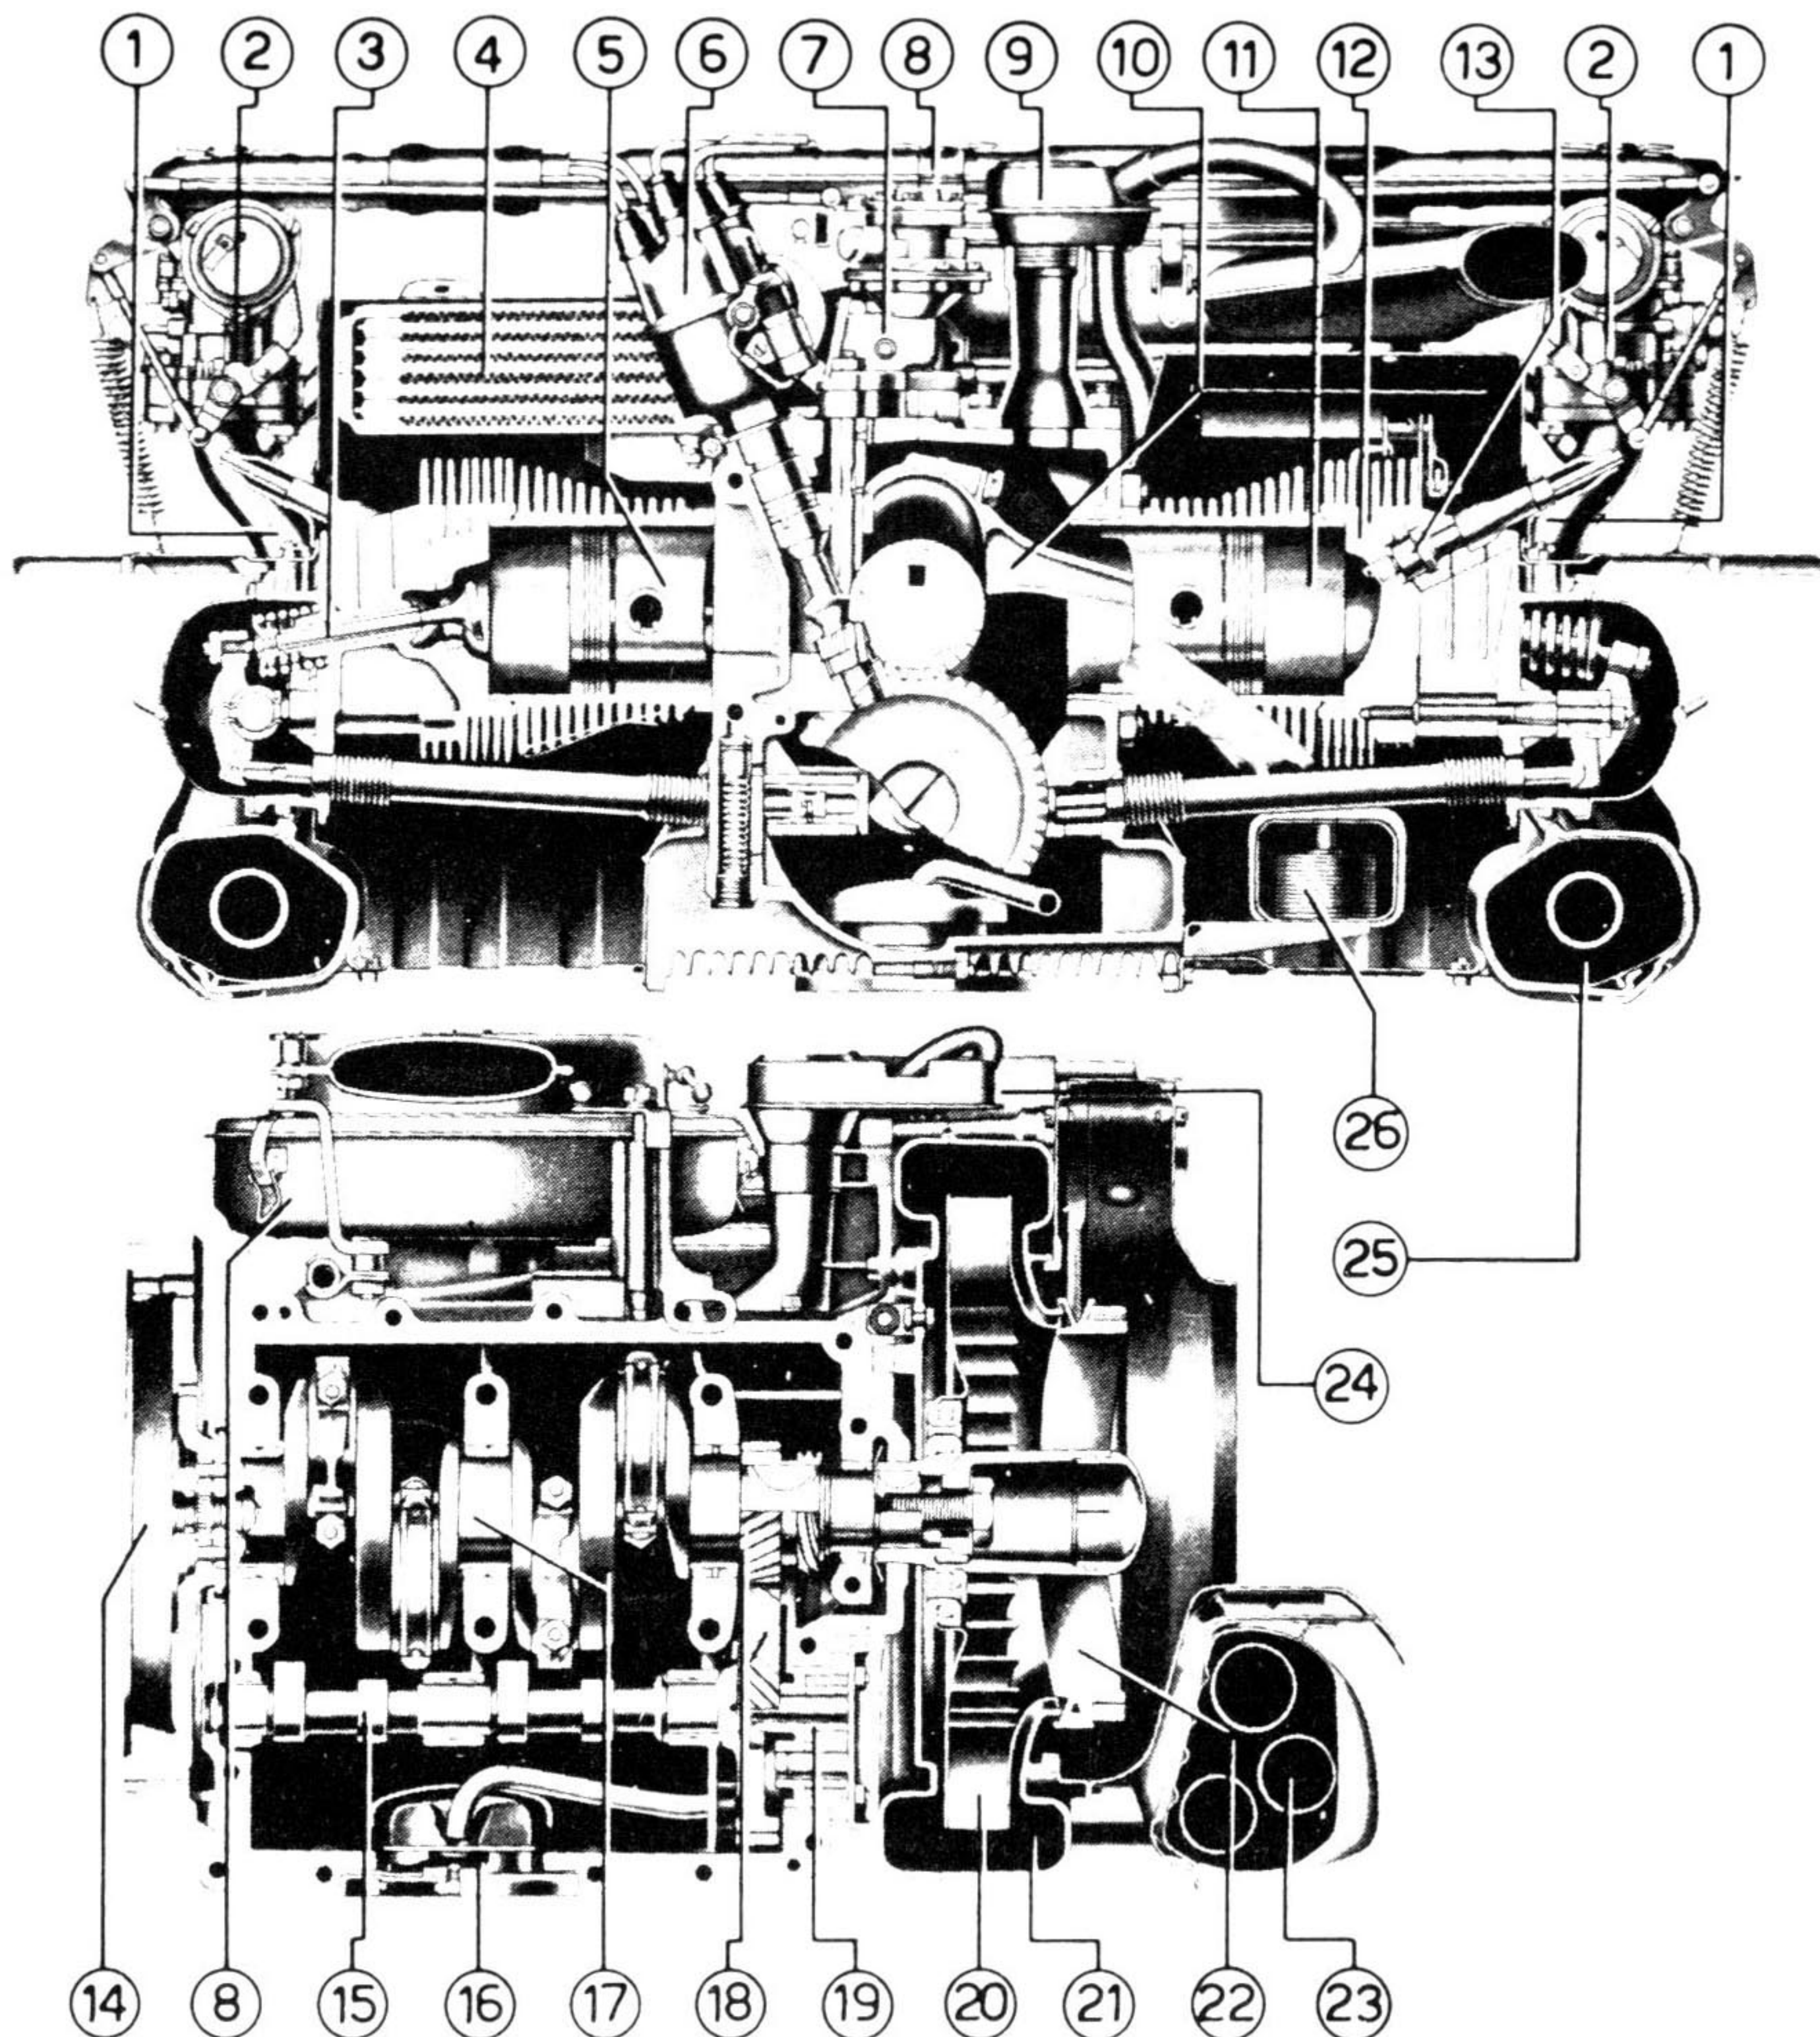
V — O motor plano “1 600” visto em dois cortes
